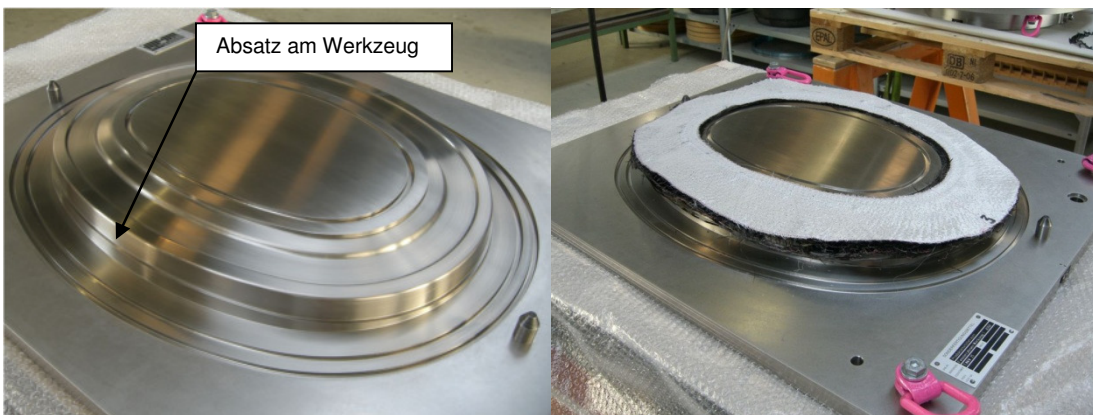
Das RTM-Werkzeug mit Absatz für das Anlegen der Preforms (links) und das bestückte RTM-Werkzeug (rechts)
